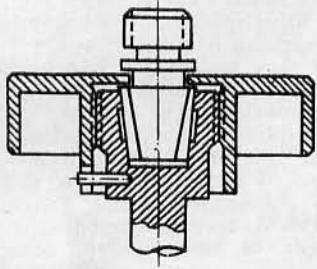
Разрез приспособления для быстрого крепления камеры к штативу
